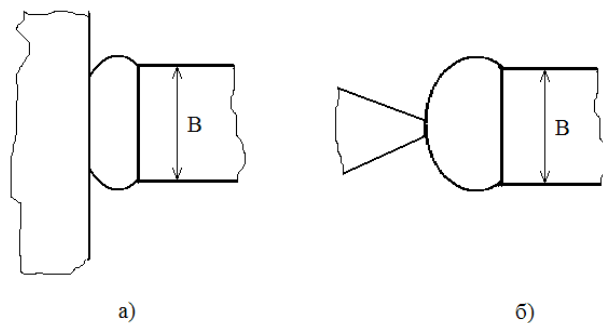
Обработка плоской поверхности (а) и поверхности небольшой протяженности - выступа шероховатости (б)
